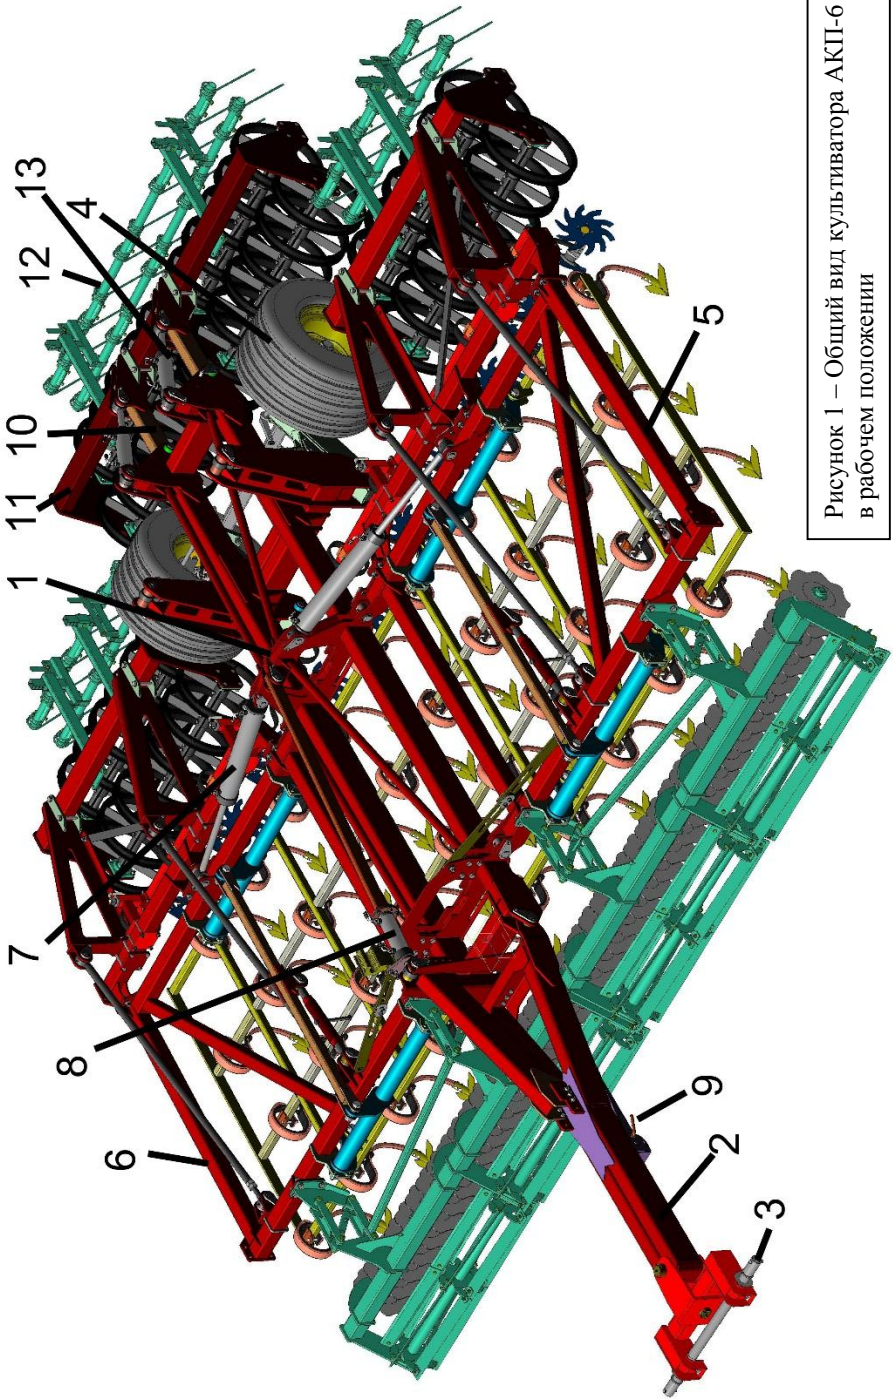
Общий вид культиватора АКП-6 в рабочем положении
